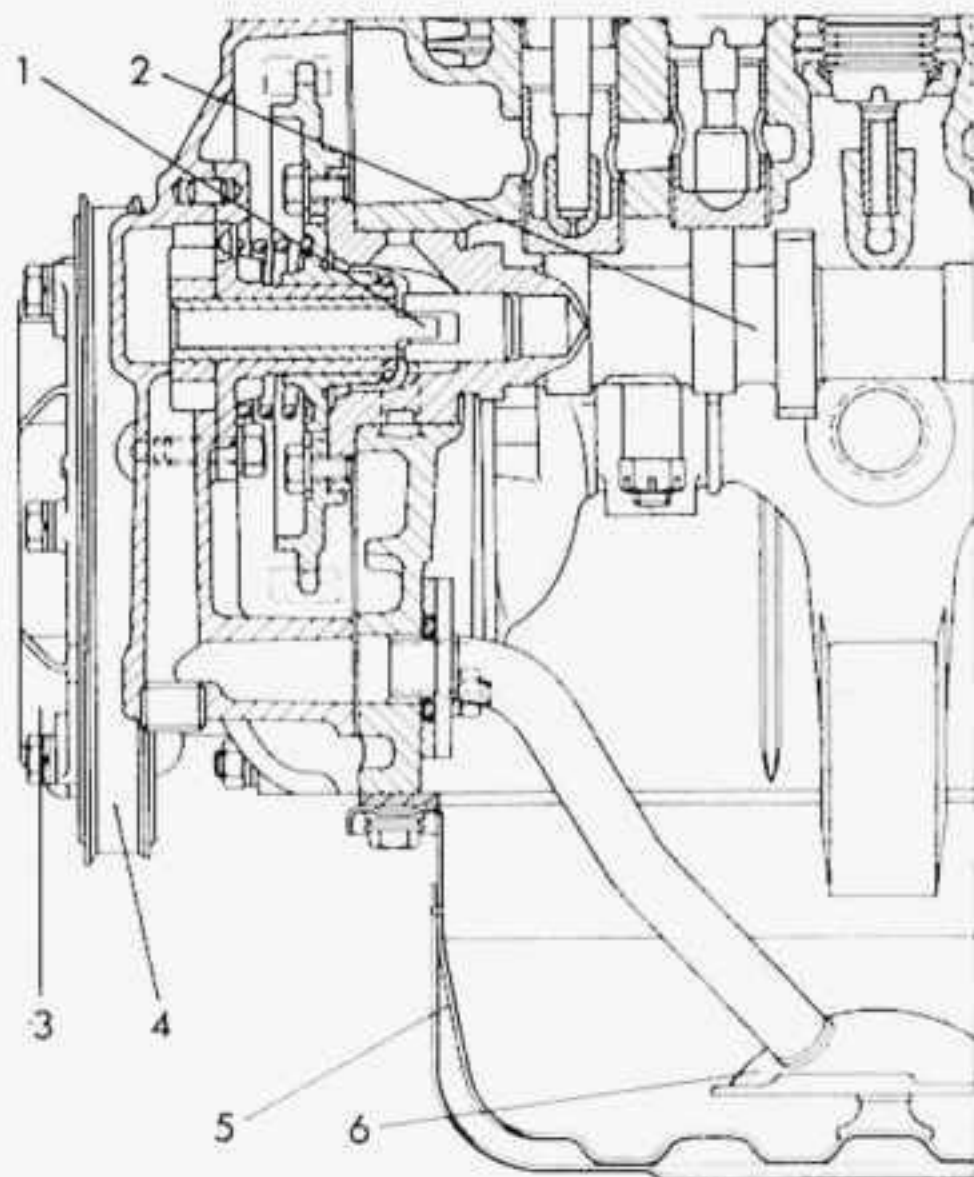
Schnitt durch die Ölpumpe und Teil des Motors
